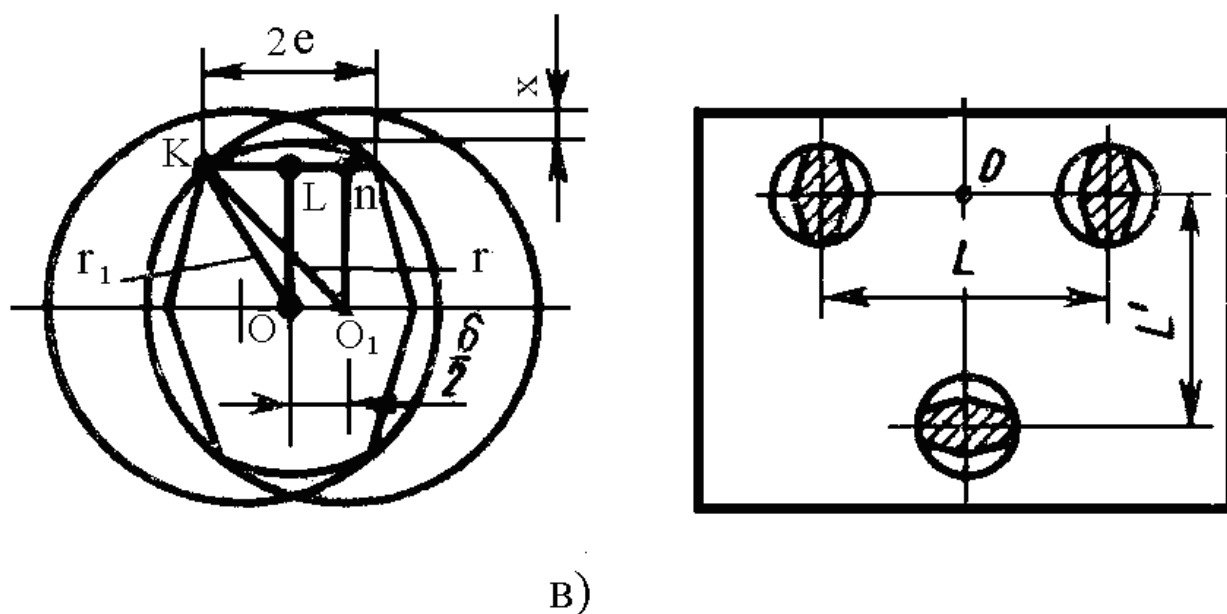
Схема установки заготовки базовыми отверстиями на пальцы
